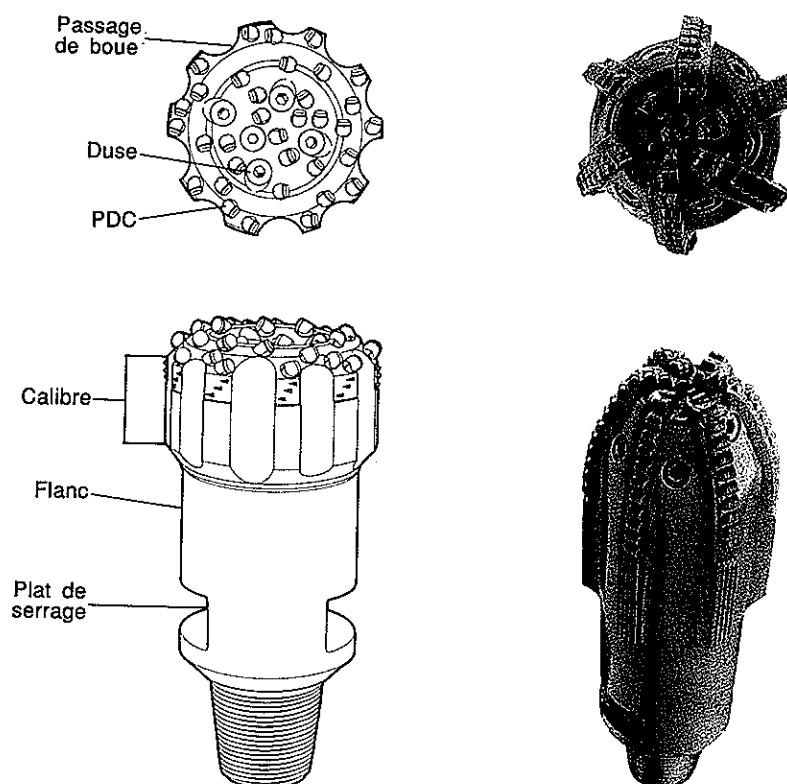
Exemples d'outils PDC (Source : Reed Tool Co.).
